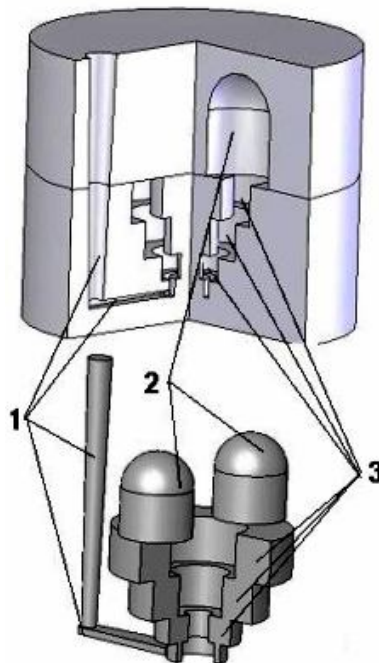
Схема процесу вилівка заготовів маточин зубчастих коліс з використанням східчастої циліндричної форми: 1 – ливникова система; 2 – живильна система; 3 – маточини
